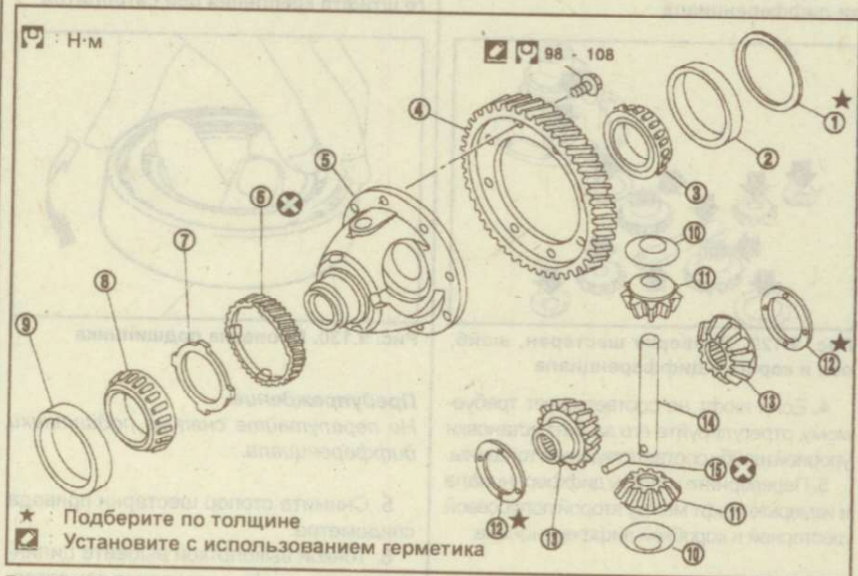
Главная передача RS5F70A: 1 – регулировочная шайба подшипника дифференциала; 2 – наружное кольцо подшипника дифференциала; 3 – подшипник дифференциала; 4 – ведомая шестерня главной передачи; 5 – коробка дифференциала; 6 – шестерня привода спидометра; 7 – стопор спидометра; 8 – подшипник дифференциала; 9 – наружное кольцо подшипника дифференциала; 10 – упорная шайба сателлита; 11 – сателлит; 12 – упорная шайба полуосевой шестерни; 13 – полуосевая шестерня; 14 – ось сателлитов; 15 – цилиндрический штифт
